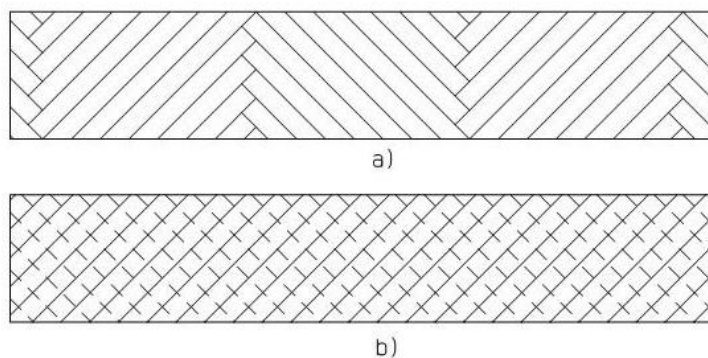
Seqüência do posicionamento do reforço na fabricação pelo processo de enrolamento filamental: a) bobinagem cruzada, b) bobinagem por superposição de camadas.
